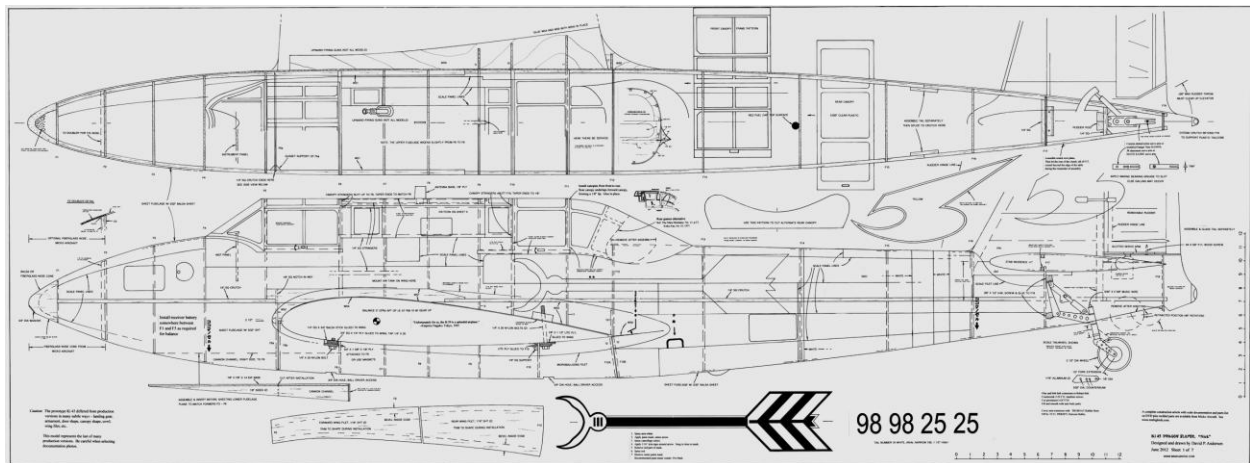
Planta y perfil parciales del Kawasaki Ki-45 Nick [6]
